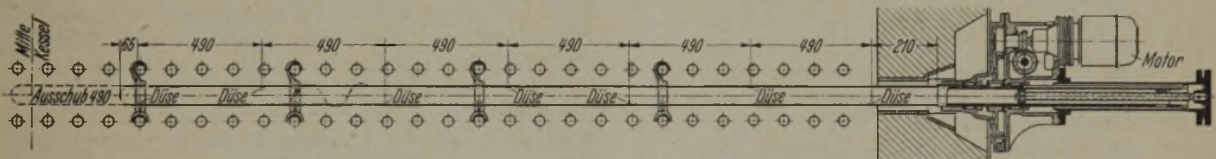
Mehrdüsenbläser mit beschränktem Vorschub zur Reinigung zurückliegender Kesselheizflächen. Werkzeugnung Ver. Kesselwerke AG., Düsseldorf.
